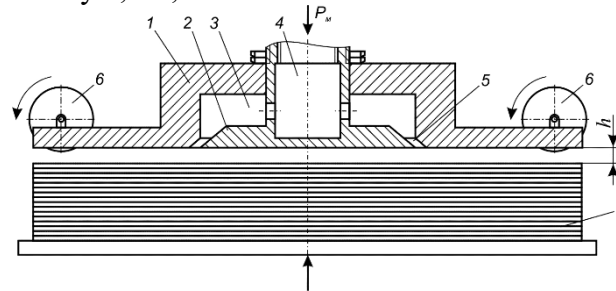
Конструкційна схема струменево-фрикційного живильника
